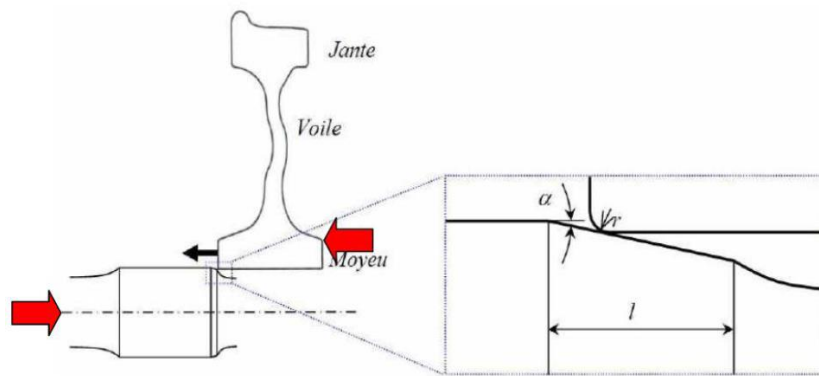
Opération de calage à la presse (assemblage) de l'essieu-axe et de la roue.
